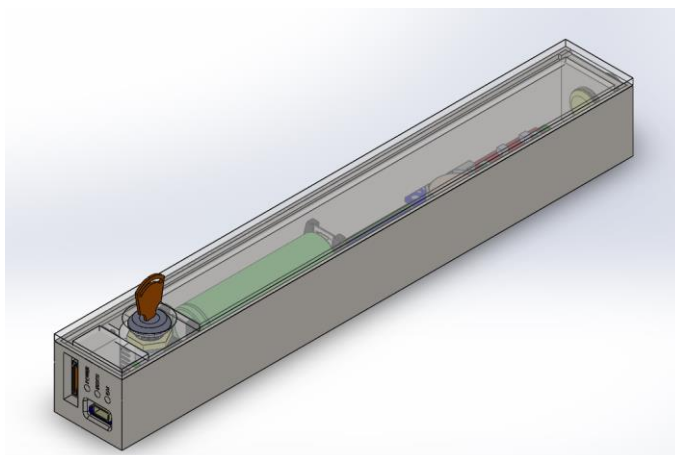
Montagem componentes eletrônicos – Vista isométrica
